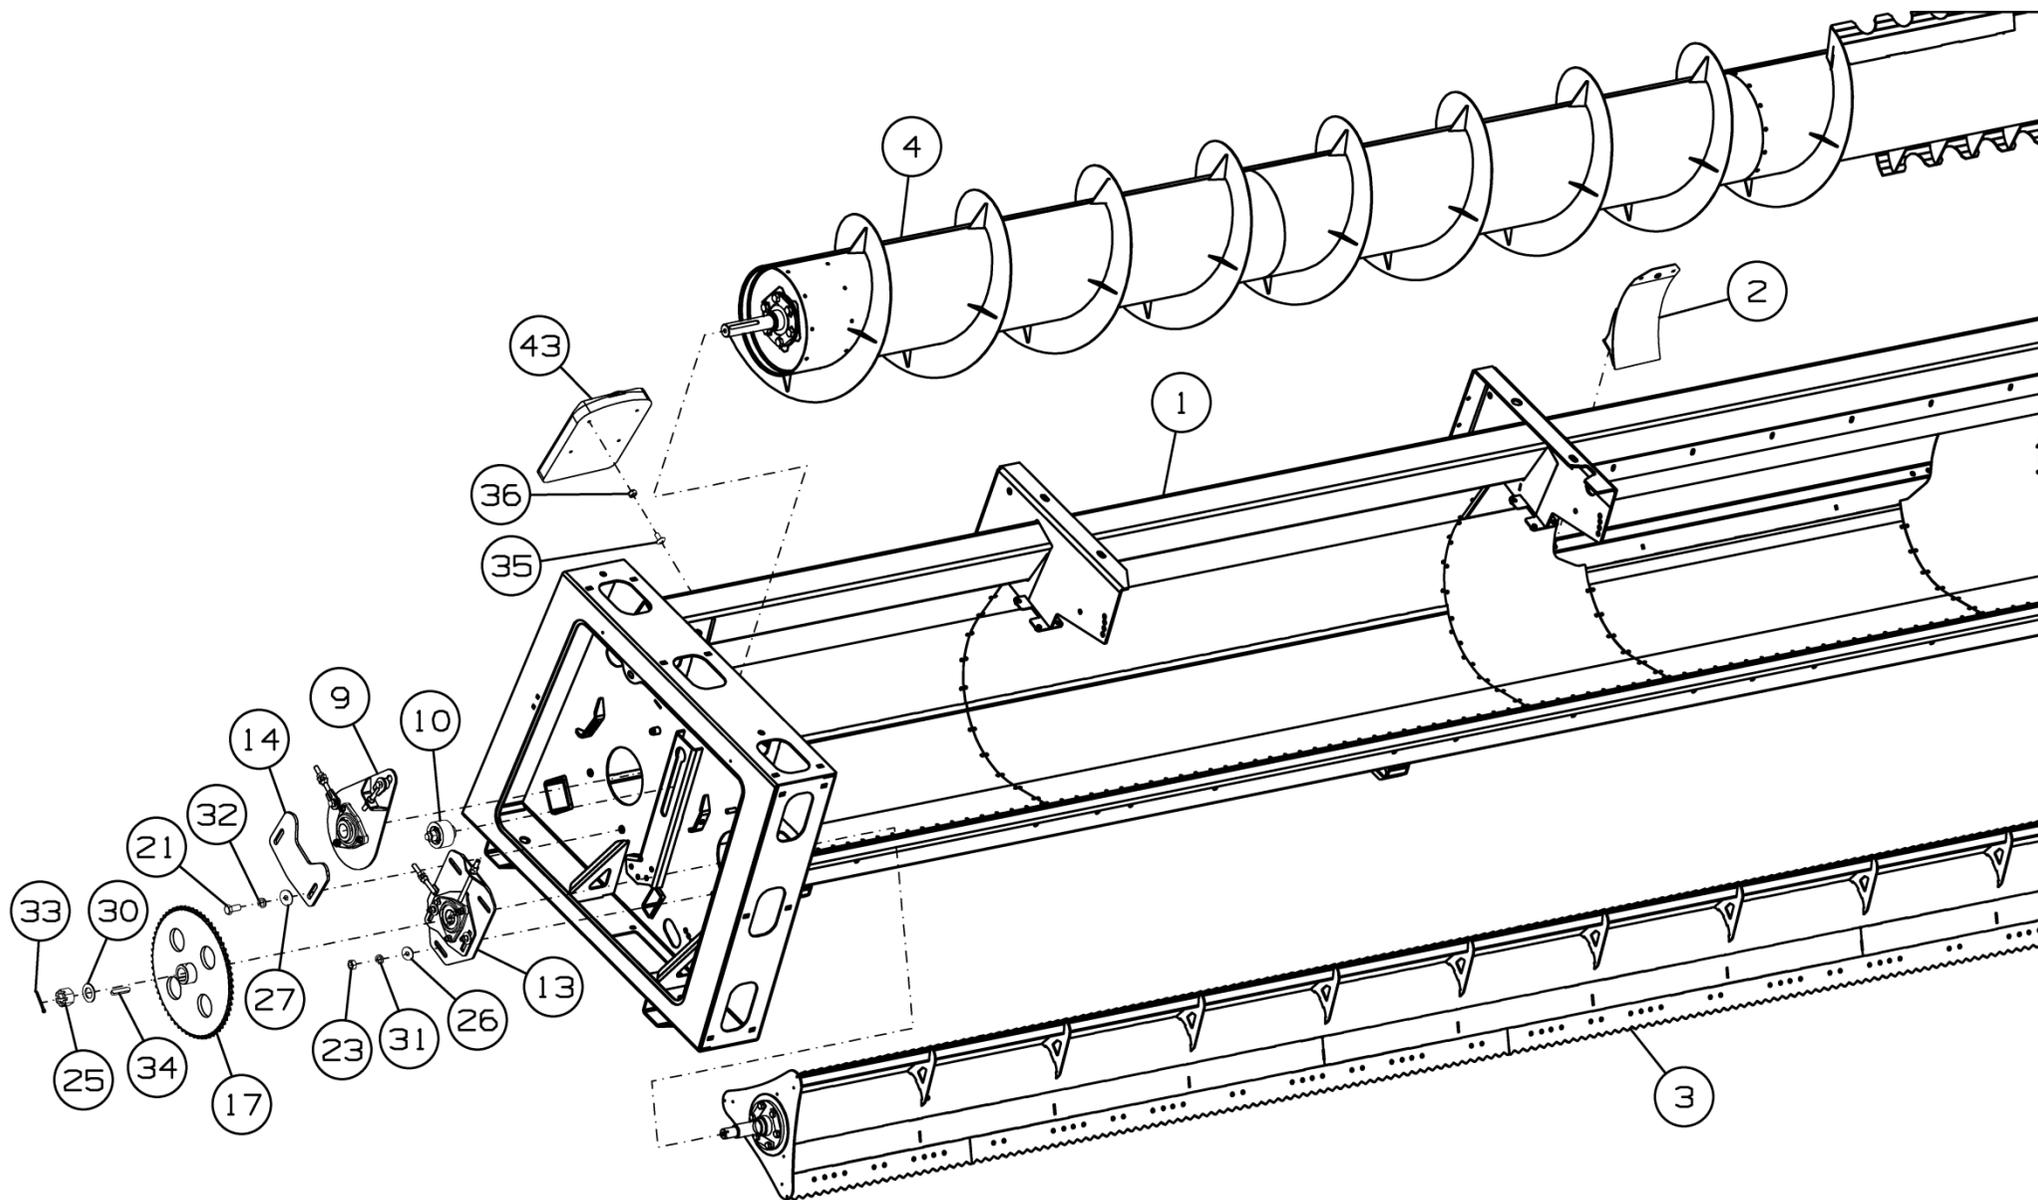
Корпус жатки SS-780.01.01.000У-01
